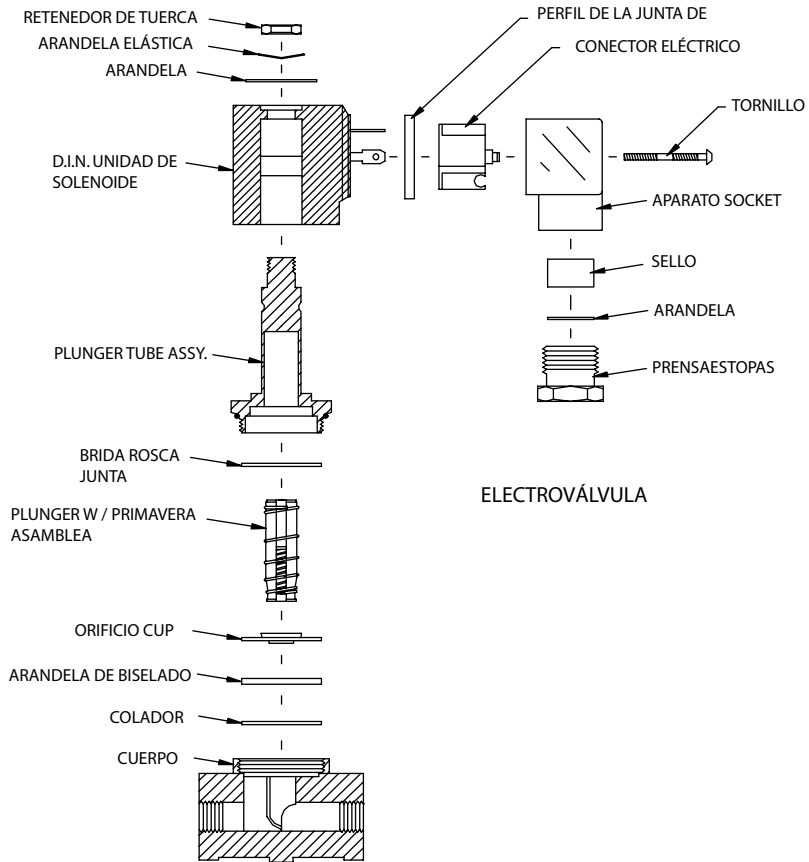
DE LA ASAMBLA DE DRENAJE DEL SOLENOIDE
